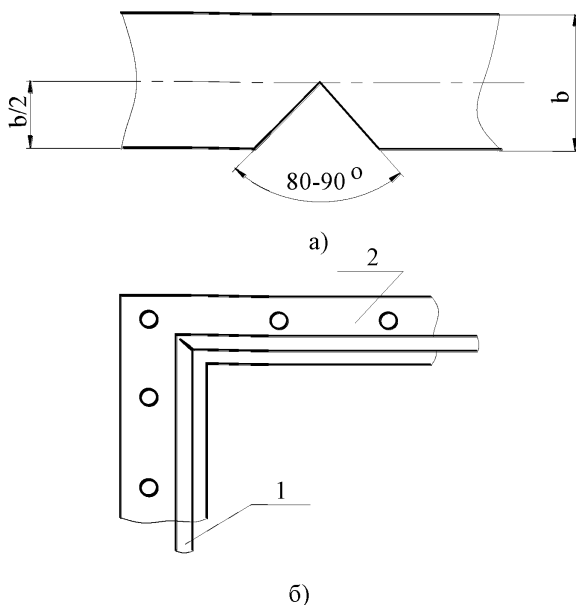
Дообработка ленты в углах уплотнительной поверхности фланца:
